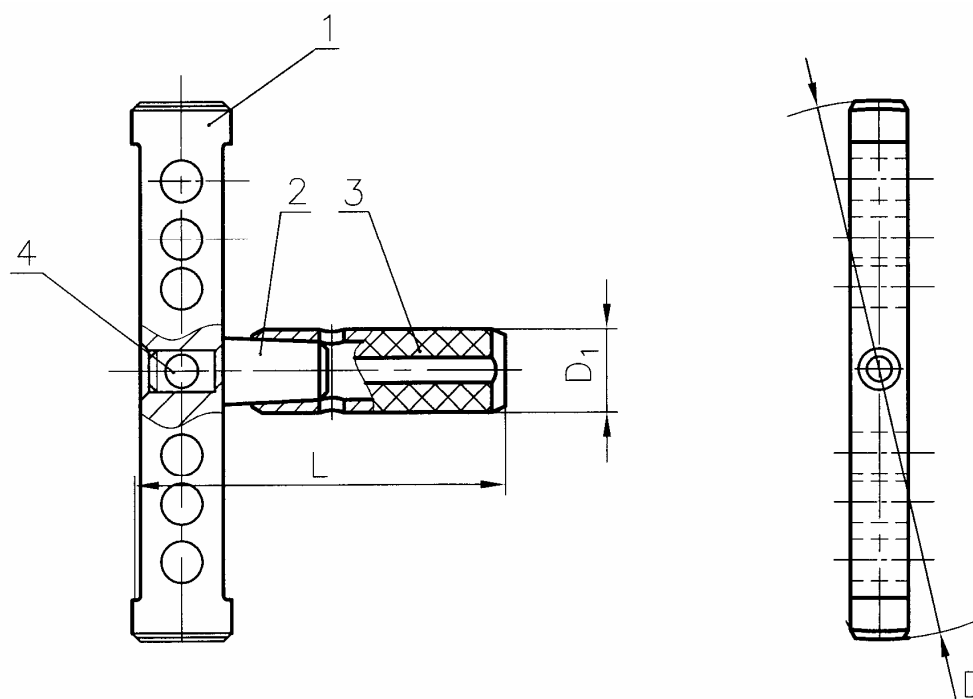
Калибр-пробка гладкий непроходной неполный:
